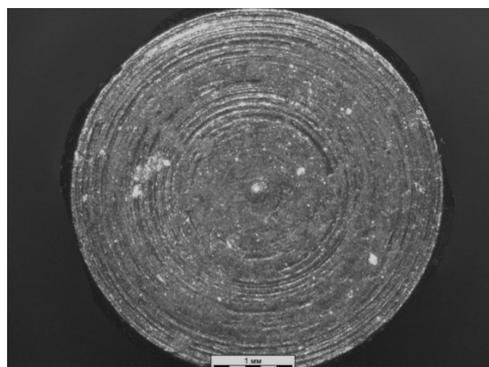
Рабочая поверхность посадочного штока капсюлятора
